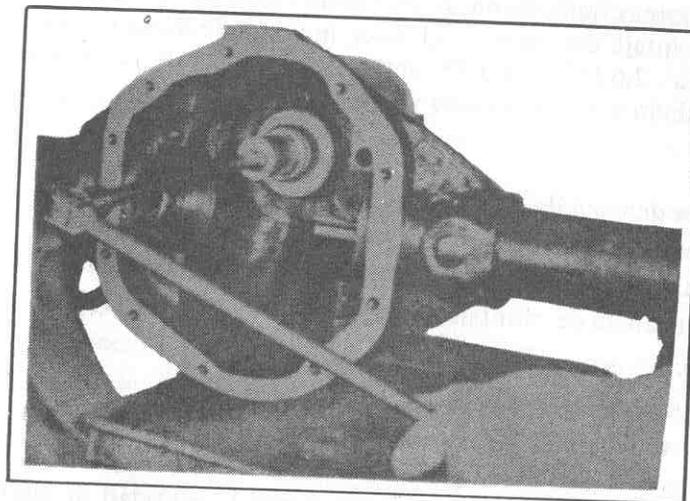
Montaje de la cubeta del cojinete delantero.
